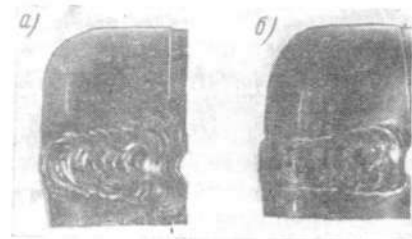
Внешний вид швов, выполненных ручной аргоно-дуговой сваркой: а — при пониженной скорости сварки; б — при очень малой скорости сварки с перегревом.
